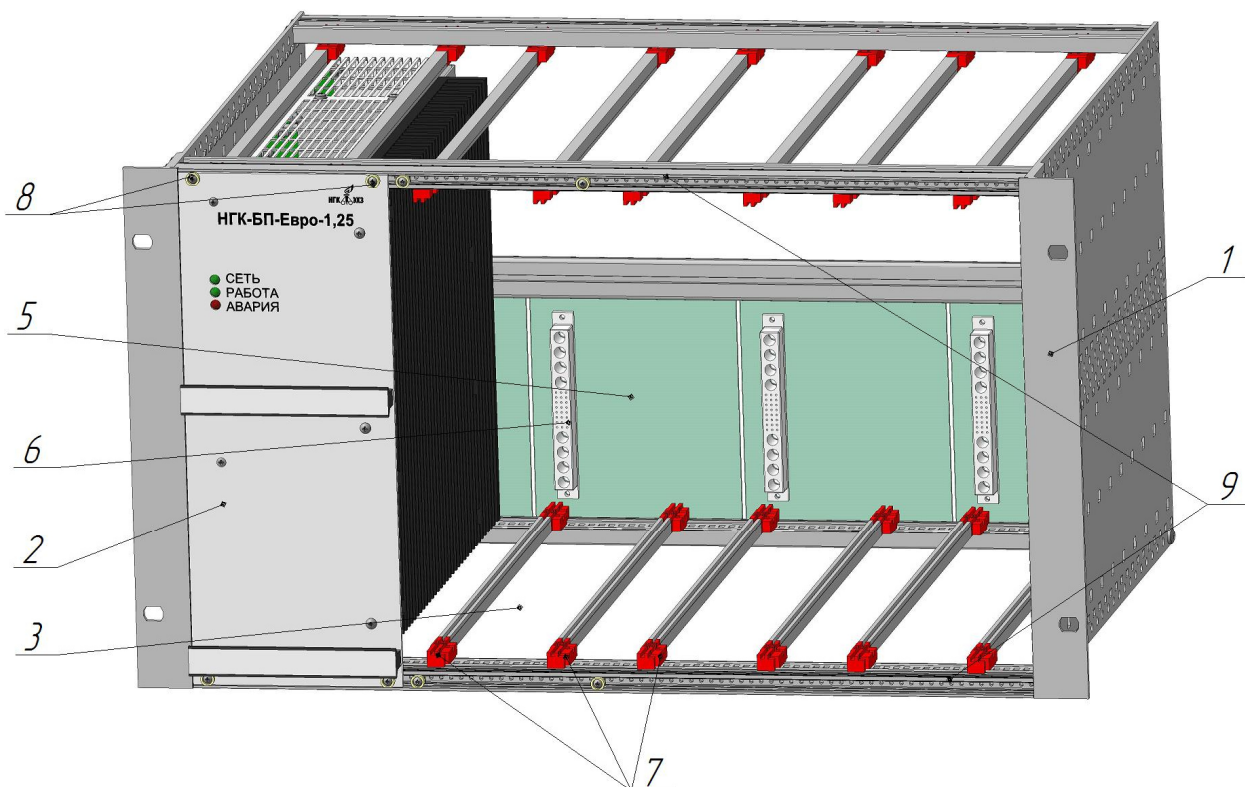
Общий вид блочного каркаса преобразователя НГК-ИПКЗ-Евро для модулей силовых НГК-БП-Евро-1,0
